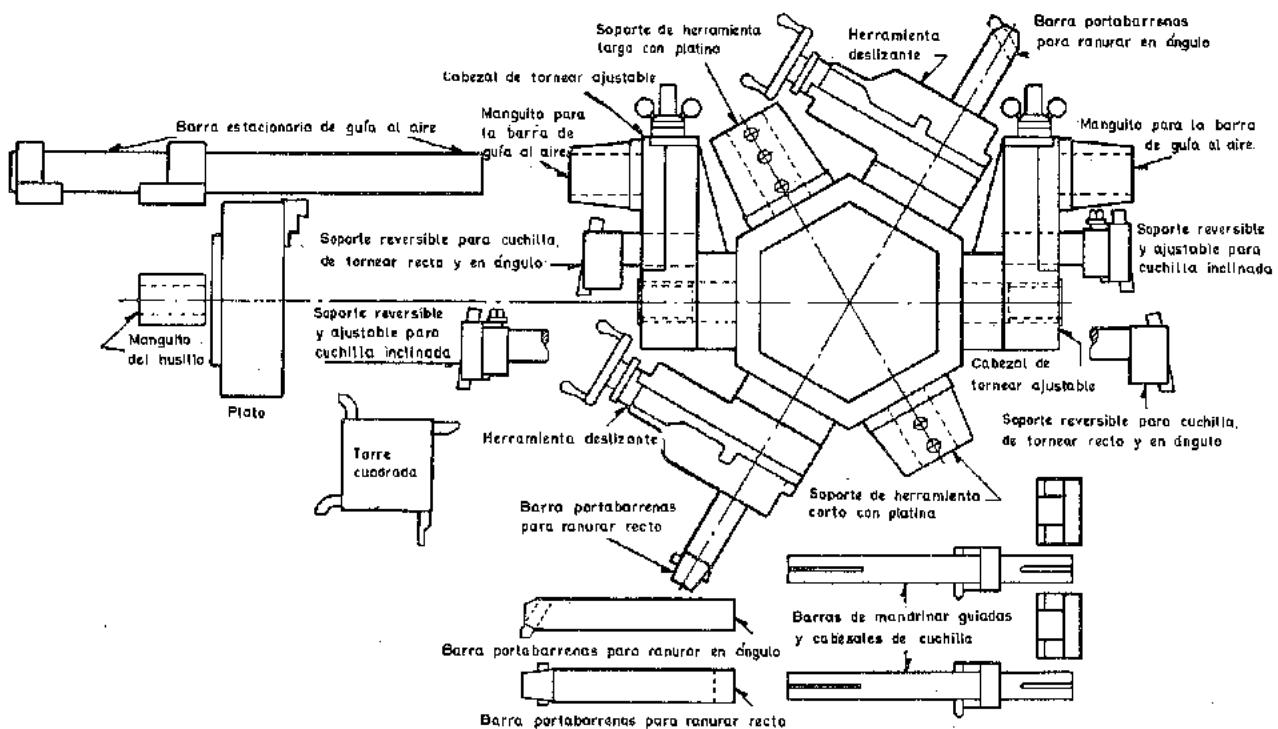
Montaje permanente del equipo universal para trabajos sobre piezas estacadas en el plato del tornillo (Warner & Swasey Co.)
